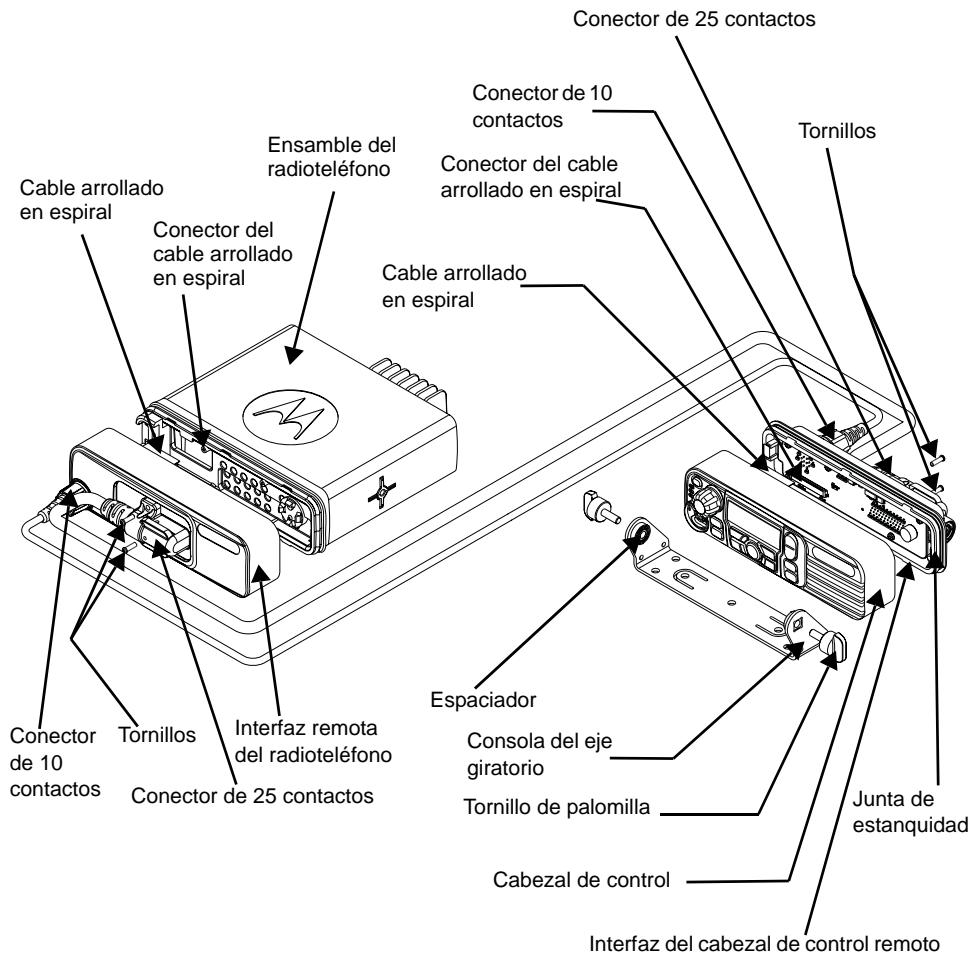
Ensamble del cabezal de control remoto y montaje del eje giratorio
